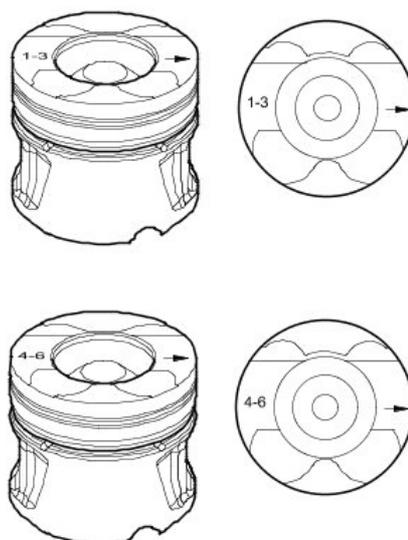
Поршни дизельного двигателя 2.7 TD V6
